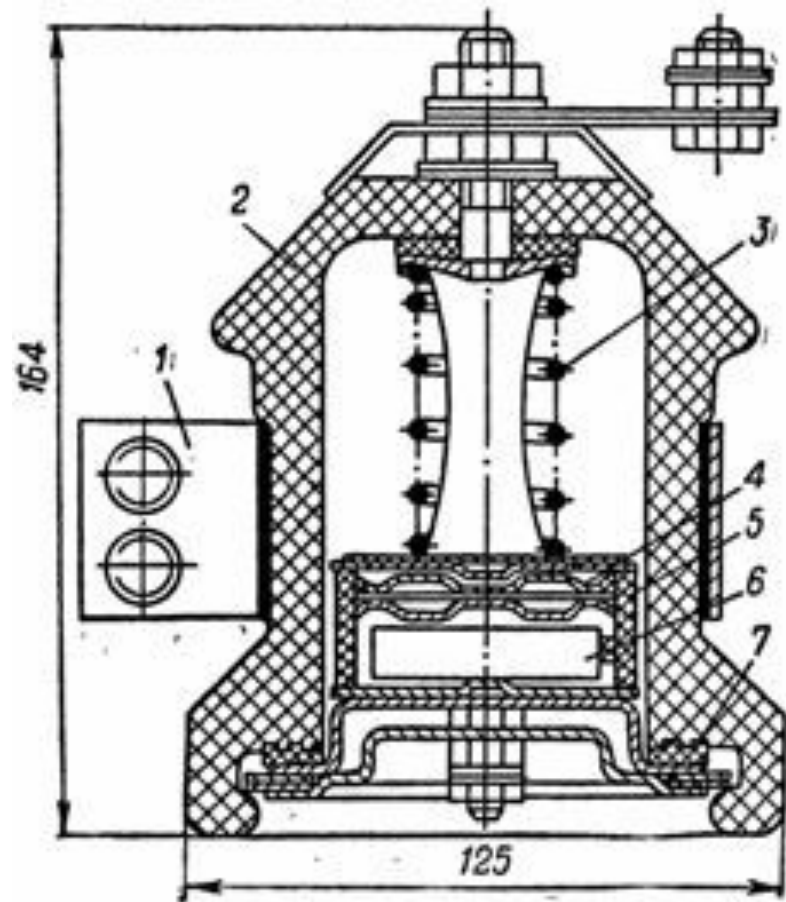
Вентильный разрядник РВН-0,5: 1 — хомут для крепления; 2 — изолятор; 3 — пружина; 4 — одиночный искровой промежуток; 5 — бумажно-бакелитовый цилиндр; 6 — диск рабочего резистора; 7 — герметизирующее резиновое кольцо
